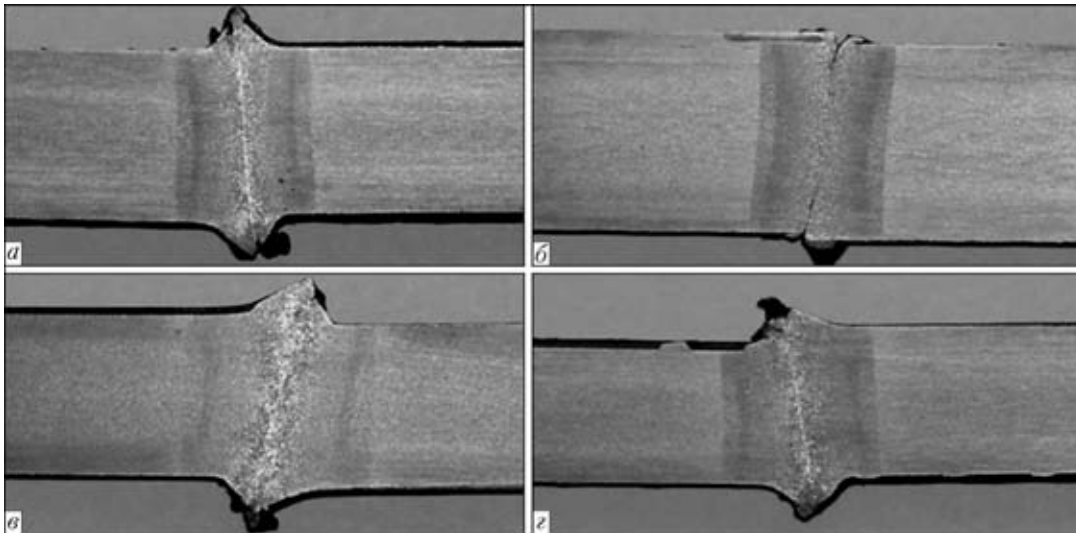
Макрошлифы стыков, полученных на различных режимах сварки: здесь и далее на рис. 2 и 3 *a* — оптимальный; *б, в* — соответственно пониженные скорость и напряжение; *г* — увеличенный вылет
